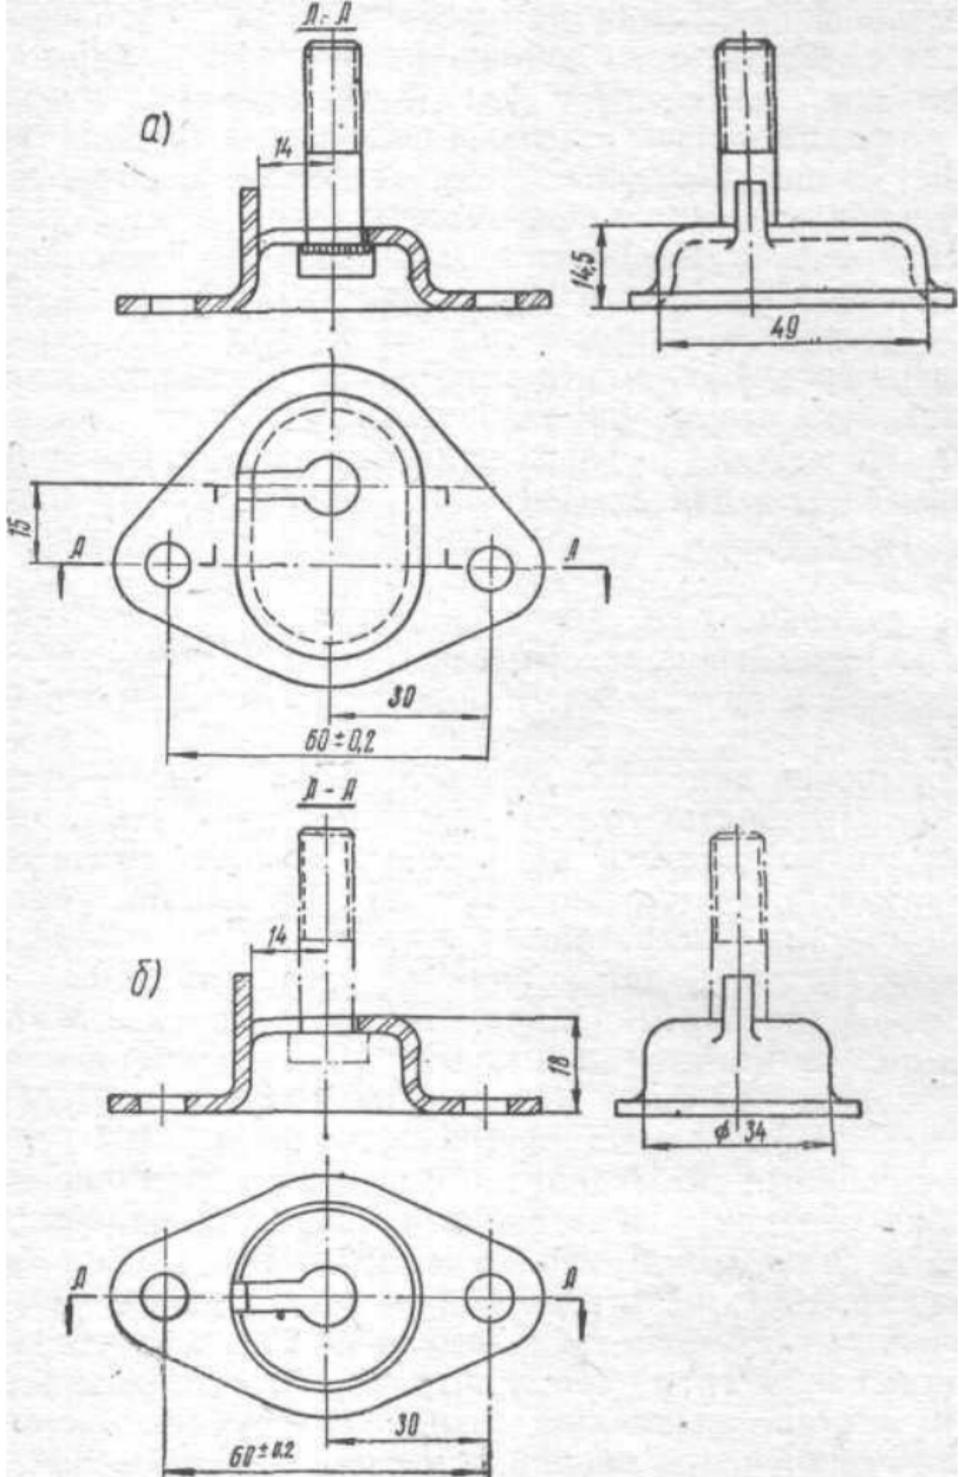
Переходные детали узла крепления передних опор двигателя:
